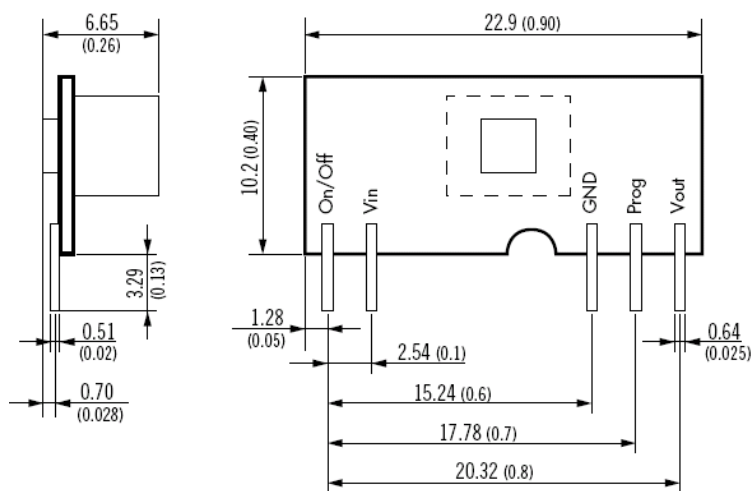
Чертеж корпуса моделей TOS 06-05SIL, TOS 06-12SIL
